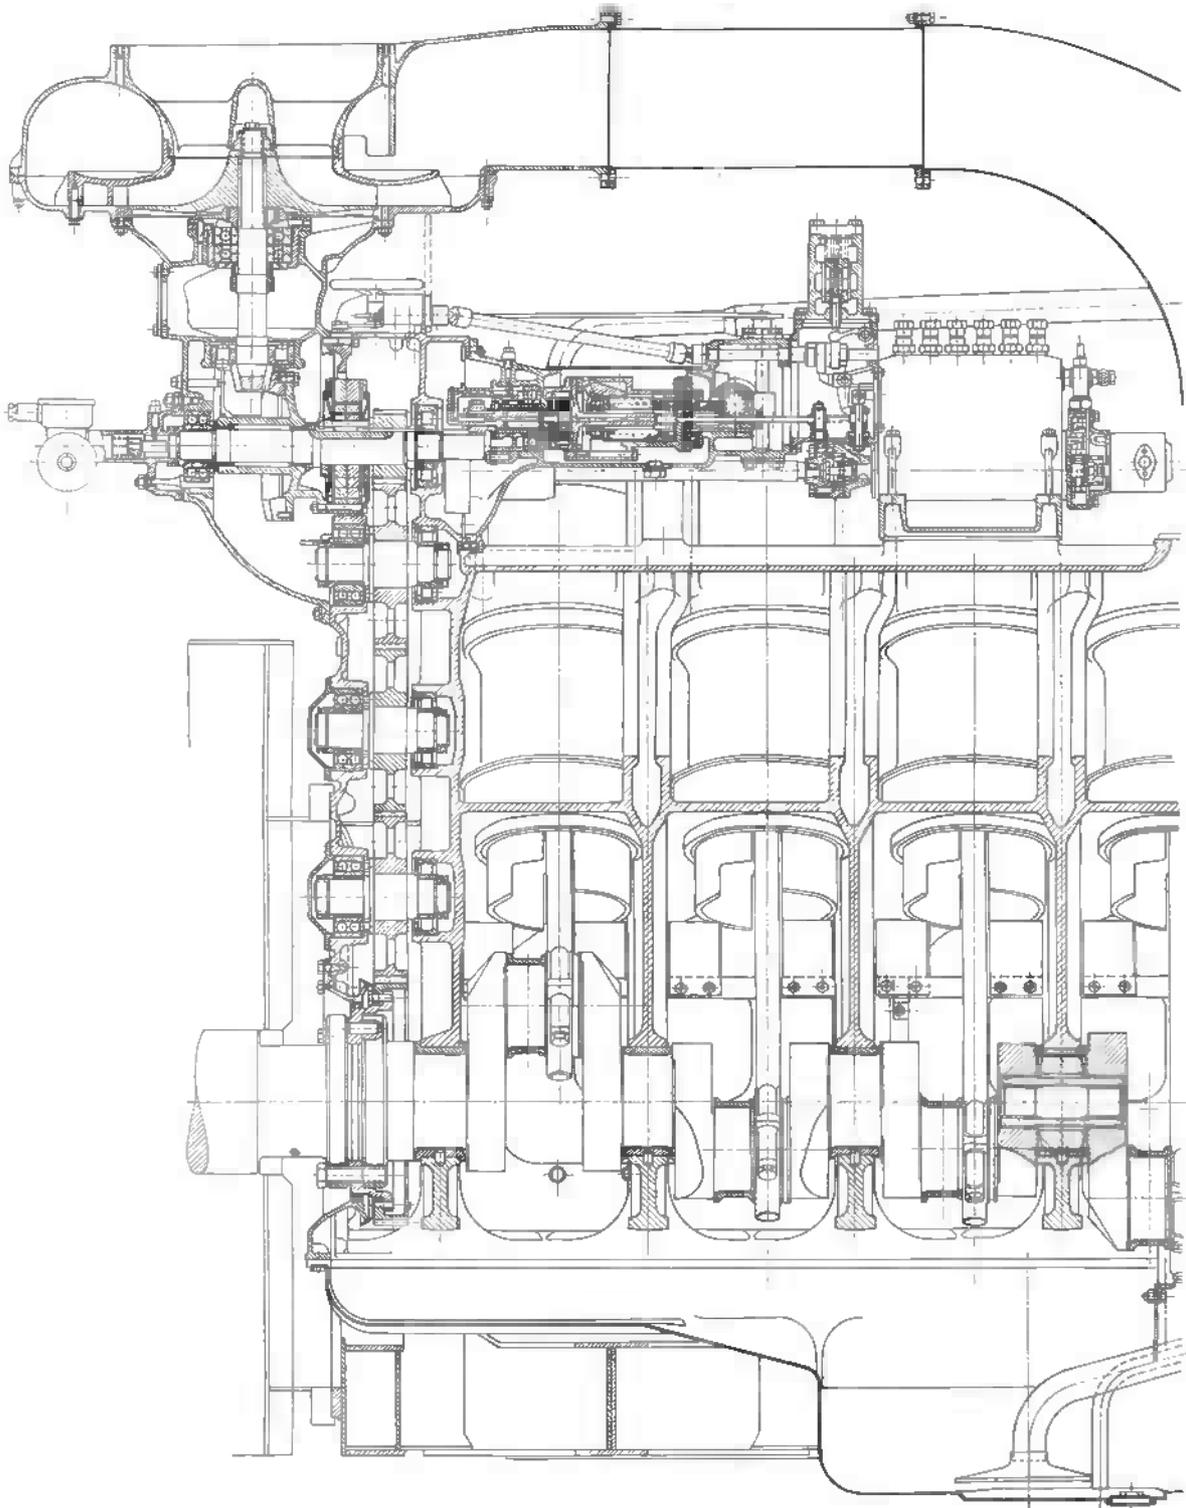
Regler, Einspritzpumpen- und Gebläseantrieb des Triebwagenmotors T 12 133 der Kieckner-Humboldt-Deutz A. G.
